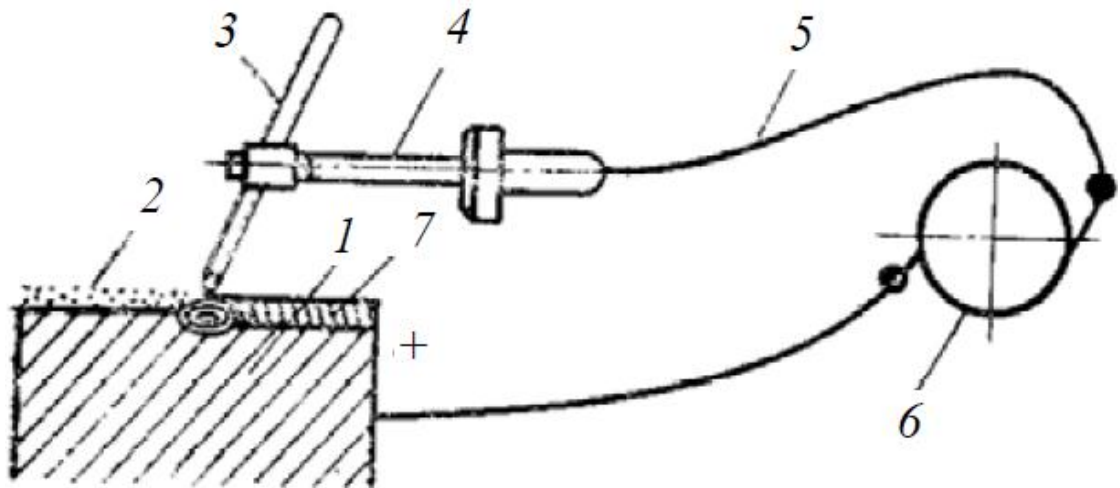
Схема підготовки дефекту до зварювання
